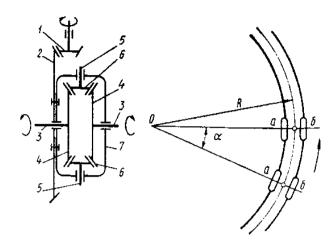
Схема главной передачи и дифференциала и траектория движения колес автомобиля на повороте: 1, 2 – шестерни главной передачи; 3 – ведущие полуоси; 4 – шестерни полуосей; 5 – оси сателлитов; 6 – сателлиты; 7 – корпус дифференциала
